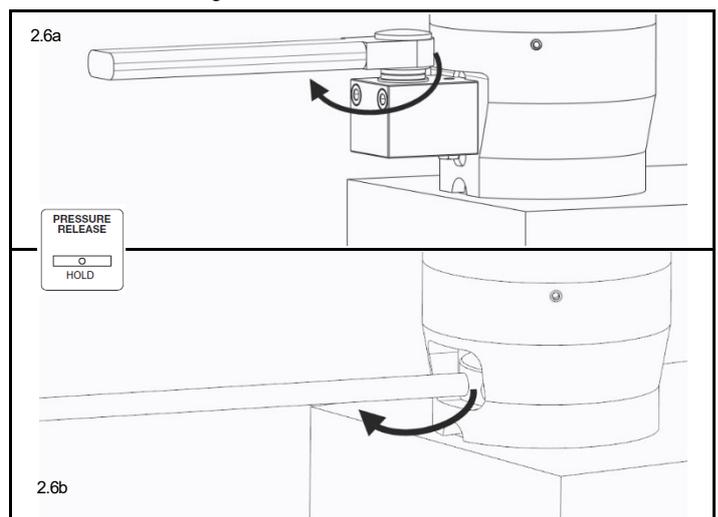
Serraggio bussola con meccanismo a ingranaggi
